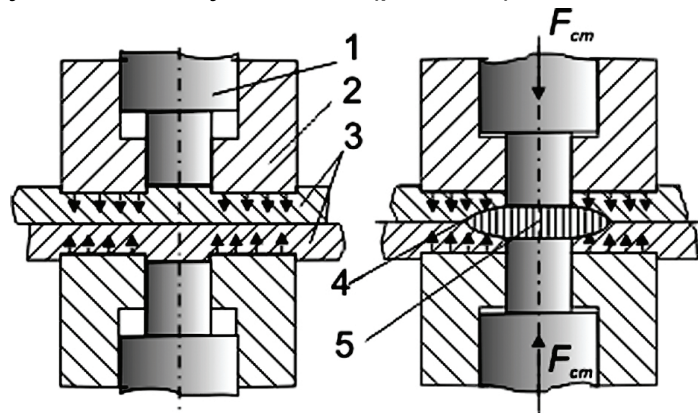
Схема зварювання з попереднім стисненням: 1- пуансон; 2 - притискач; 3 - деталі, що зварюють; 4 - периферійна зона зварювання; 5 - внутрішня зона зварювання
